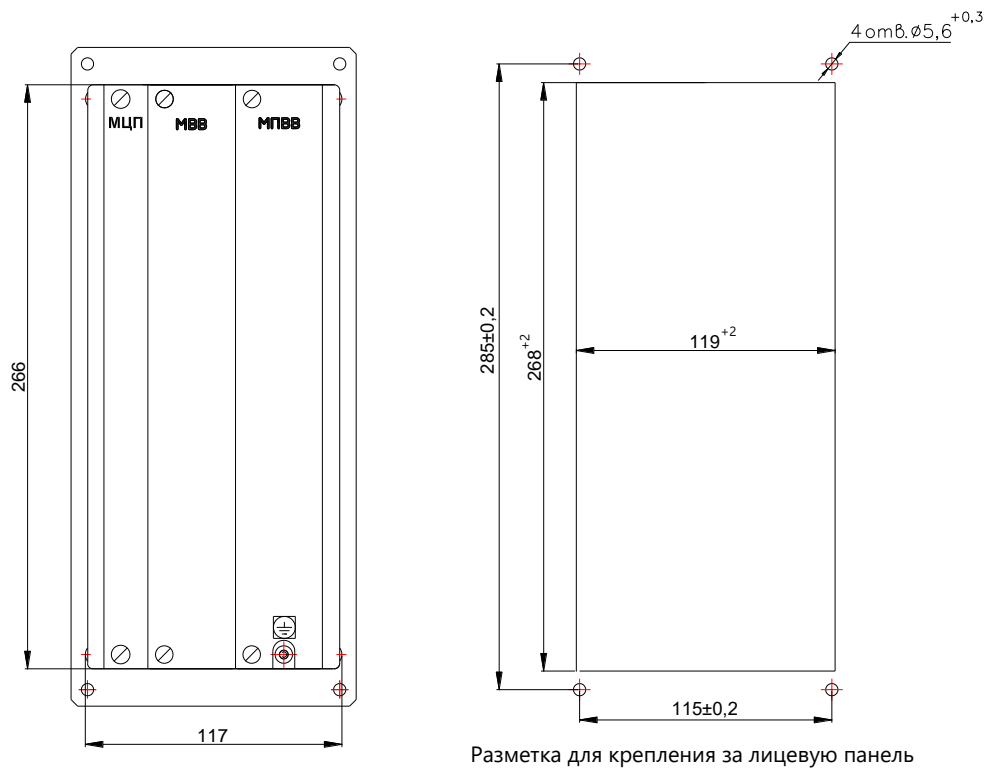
(лист 2 из 2) – Габаритные и установочные размеры
